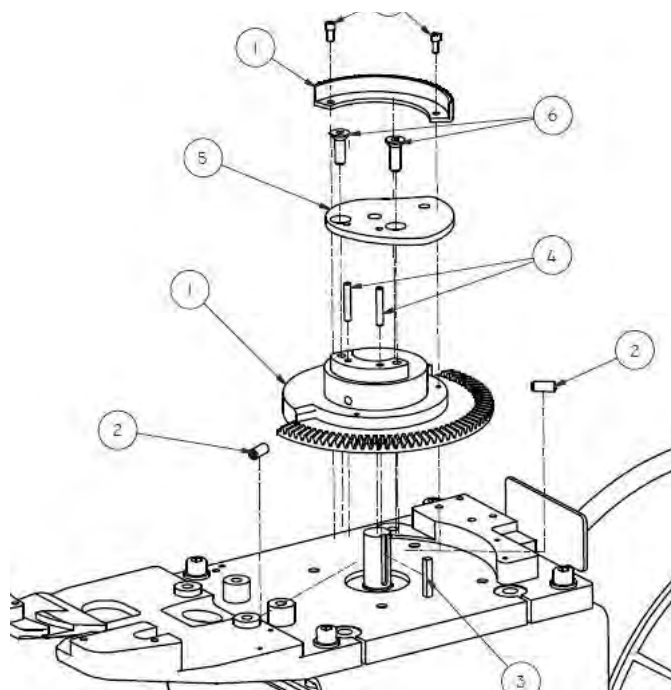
Engranaje, leva y tambor de alimentación
